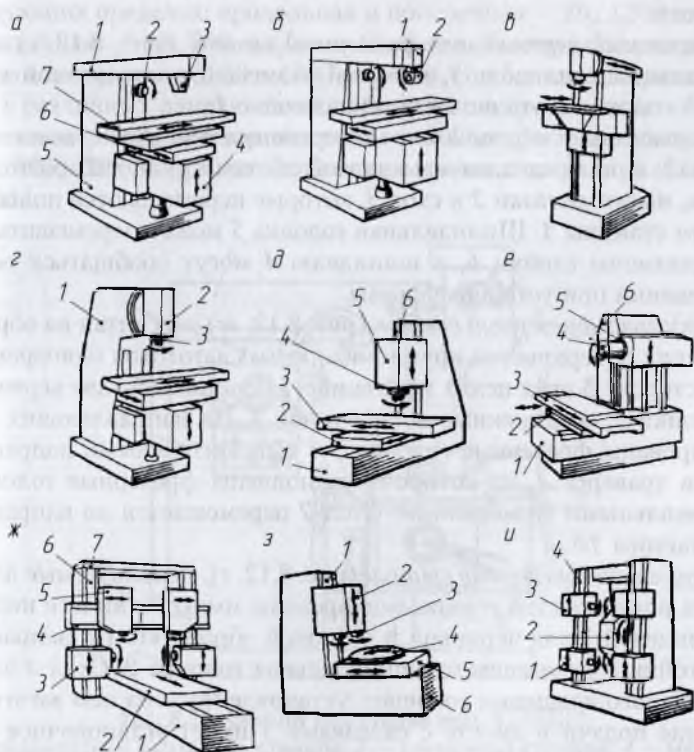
Разновидности фрезерных станков и движения на них: а, б — консольные горизонтально-фрезерные станки; в, г — бесконсольный и консольный вертикально-фрезерные станки; д, е — бесконсольные вертикально- и горизонтально-фрезерные станки; ж, з, и — продольно-, карусельно- и барабанно-фрезерные станки
